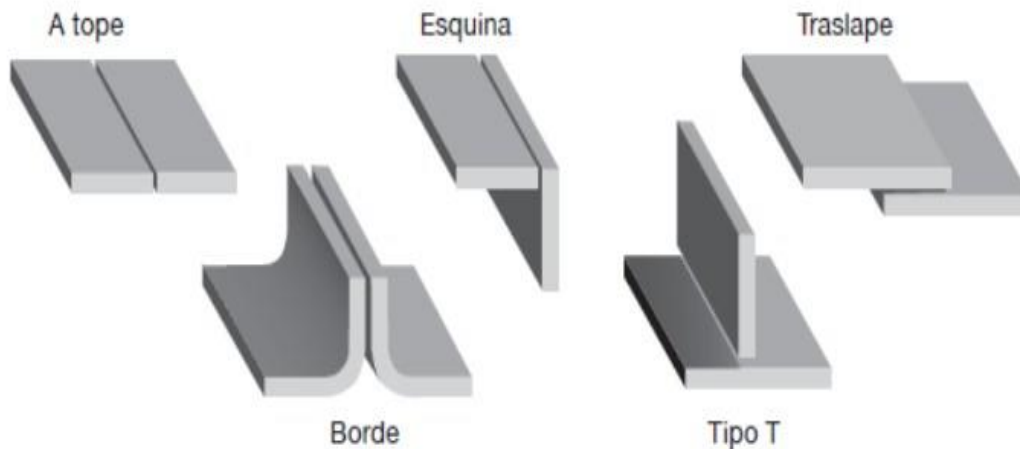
Uniones básicas o juntas de Soldadura [17]
